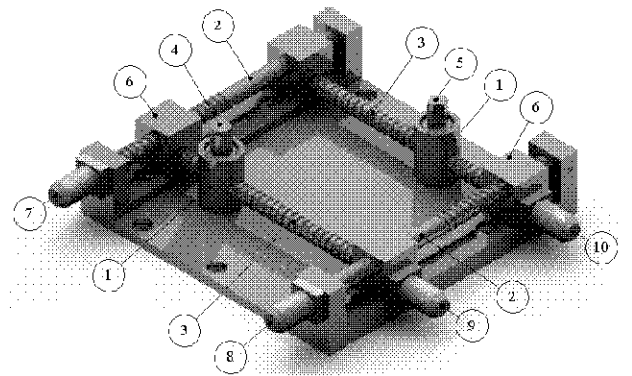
Переналагоджуваний базуючий модуль для установлення корпусних деталей за площиною та двома отворами
